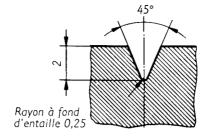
Vue agrandie de l'entaille des éprouvettes à section carrée
